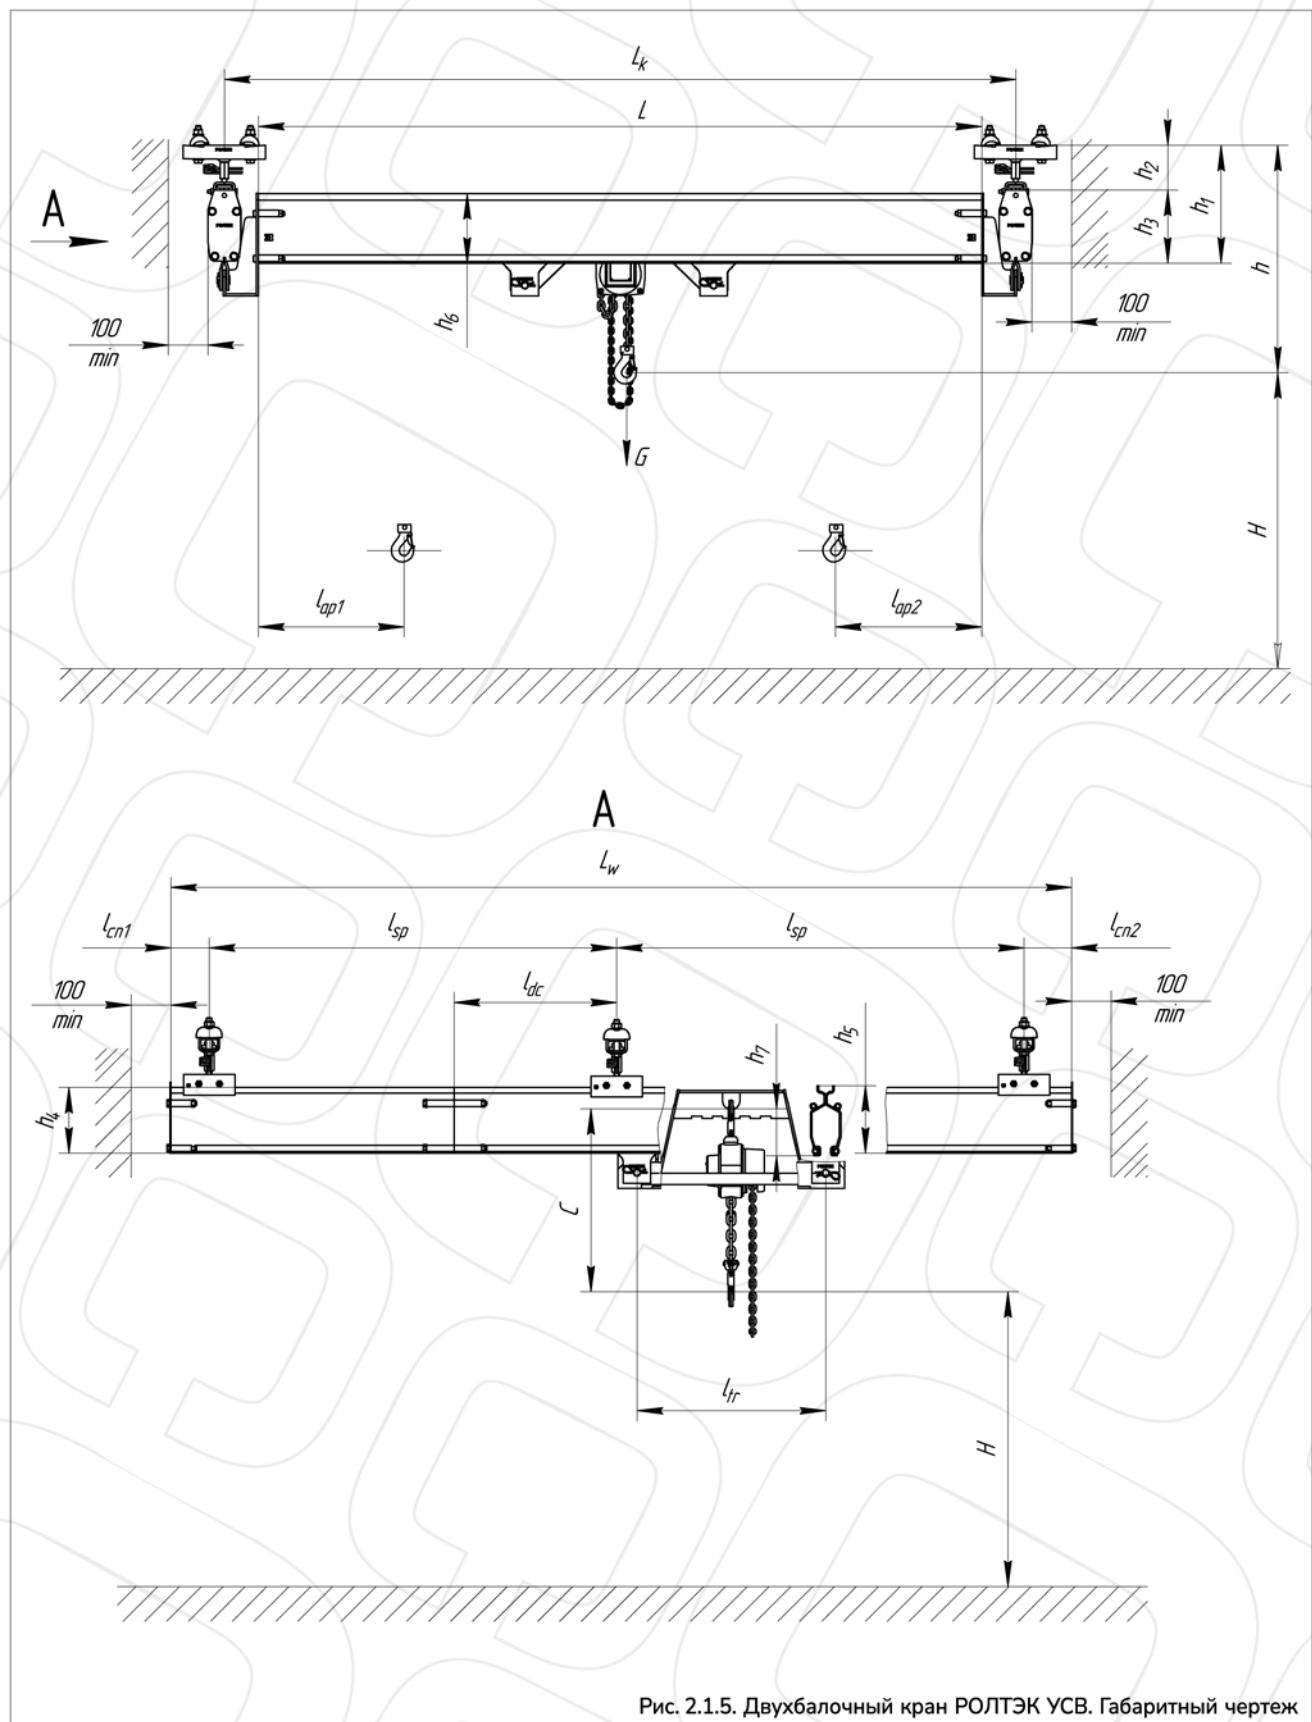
Двухбалочный кран РОЛТЭК УСВ. Габаритный чертеж
